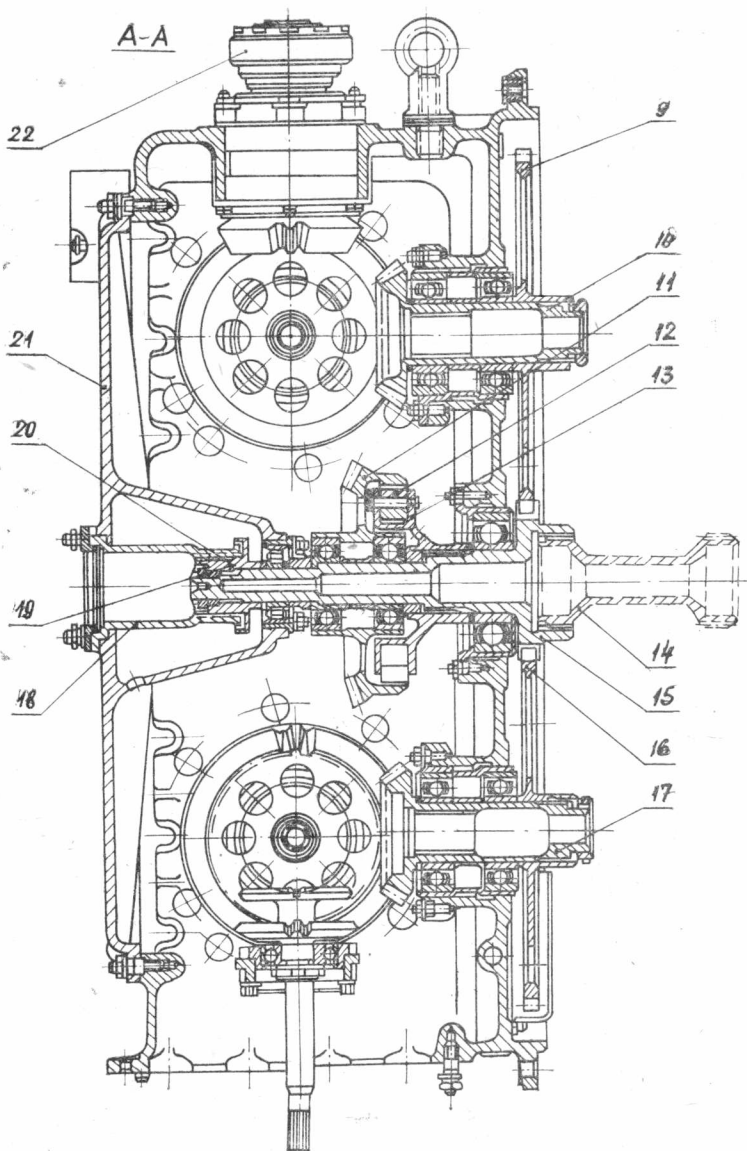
Конструкция коробки приводов: 1 — корпус; 2 — ведомые шестерни привода топливных насосов; 3 — шестерня запасного привода; 4 — рес-сора привода тахометра; 5 — ведущая шестерня стартера; 6 — ротор центрифуги; 7 — шестерня привода маслонасоса; 8 — шестерня привода центрифуги; 9 — ведомая цилиндрическая шестерня верхняя; 10 — ведущая кони-
